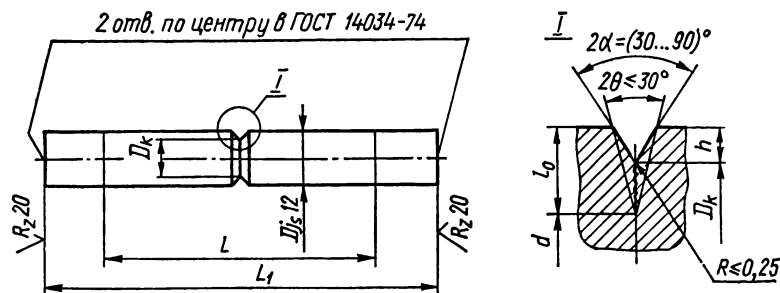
Цилиндрический образец с кольцевой трещиной для испытаний на ударное растяжение и изгиб.
